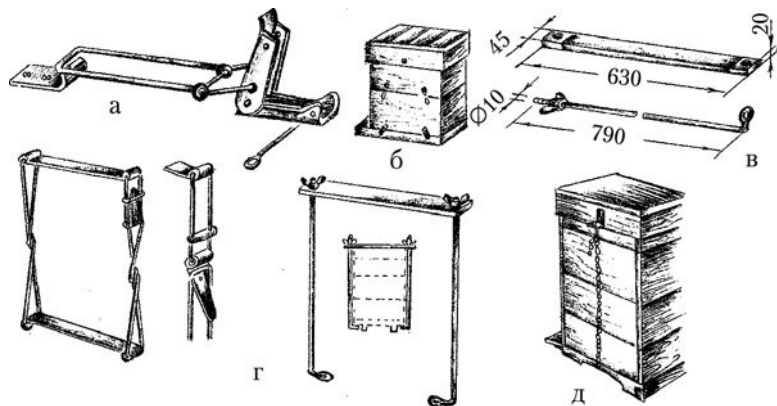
Ульевые скрепы: а – натяжной скреп; б – петли и пластинки на шурупах; в – скреп «хомут»; г – скрепы с замковым соединением; д – цепные скрепы
